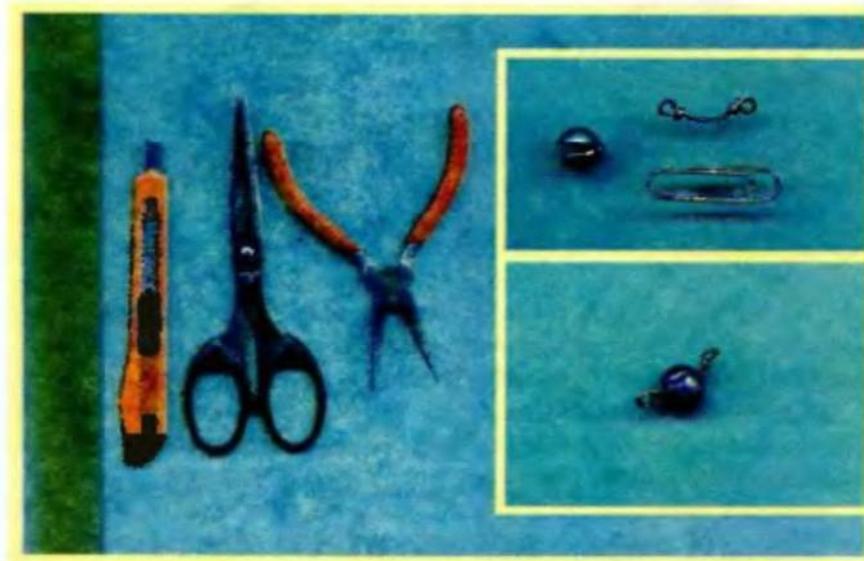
Изготовление грузила с помощью линейки, ножа, ножниц, плоскогубцев
